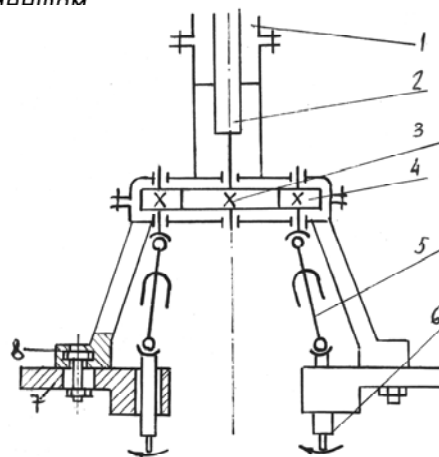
Схема универсальной головки с раздвижными шарнирными валиками: 1 – корпус; 2 – шпindel; 3 – ведущее зубчатое колесо; 4 – промежуточные зубчатые колеса; 5 – телескопический валик; 6 – рабочие шпиндели; 7 – кронштейны; 8 – корпус головки
